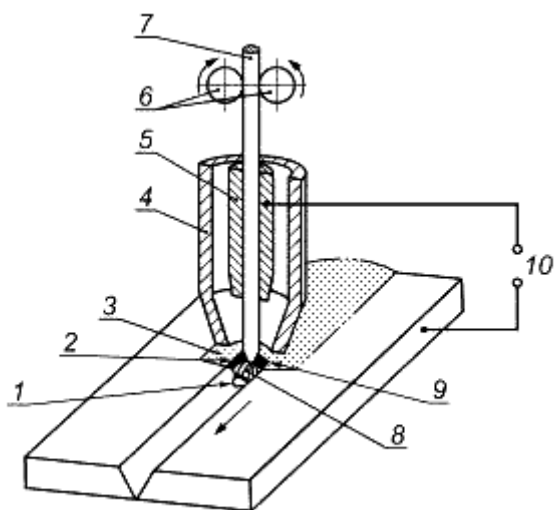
Процес автоматичного зварювання під флюсом
